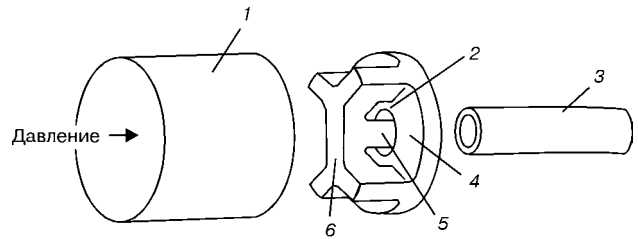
Система камерной матрицы с двумя каналами и сварочными камерами: 1 — сплошная заготовка; 2 — зона сварного шва; 3 — труба, полученная выдавливанием; 4 — матрица; 5 — выступ оправки; 6 — перемычка
